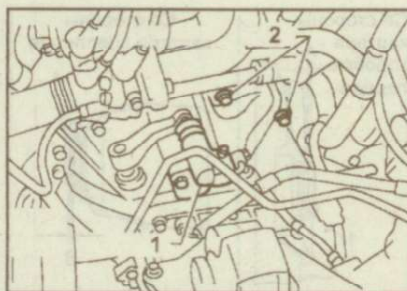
Расположение рабочего цилиндра сцепления (1) и болтов (2) крепления стартера
